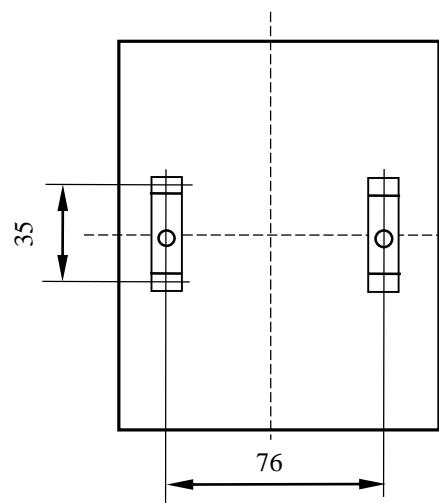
Габаритные и установочные размеры ЭП85554 с входными
